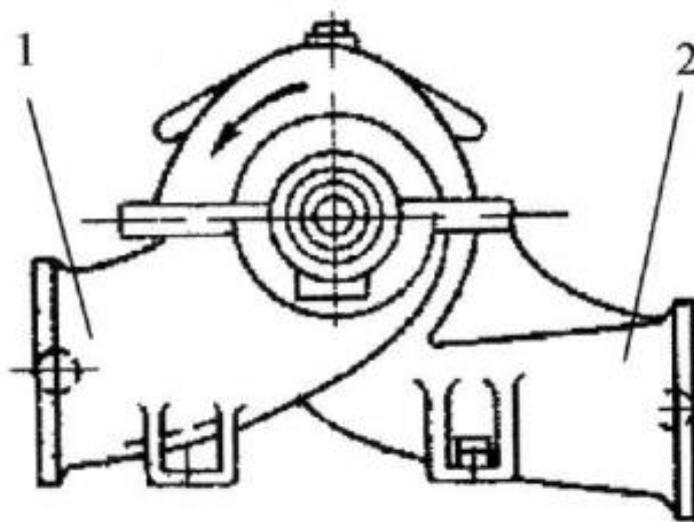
Корпус насоса с горизонтальным разъемом: 1 - всасывающий патрубок; 2 - нагнетательный патрубок
